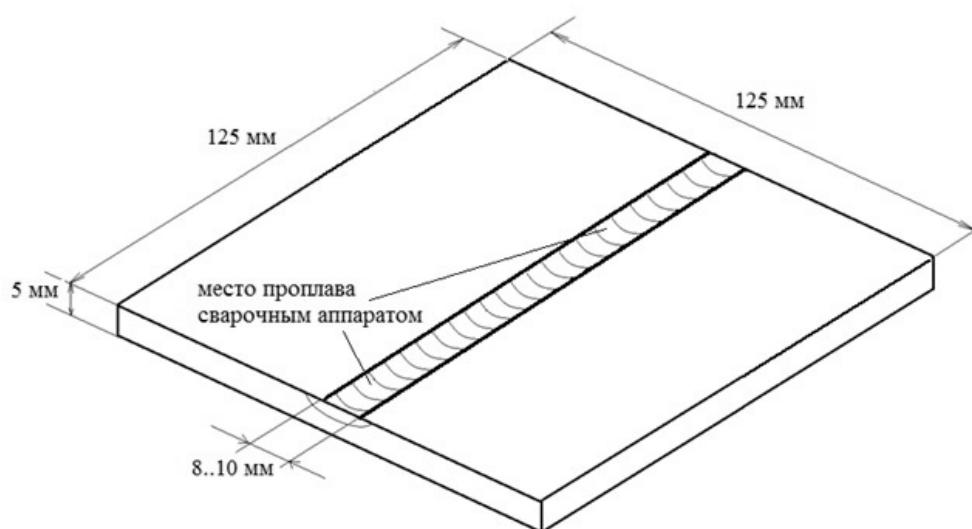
Пластина с местным проплавом сварочным аппаратом
